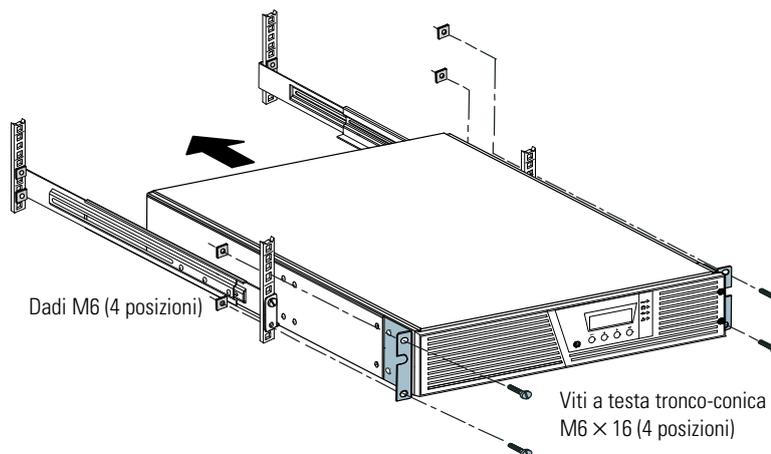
Installazione dei supporti di montaggio (vista anteriore)
